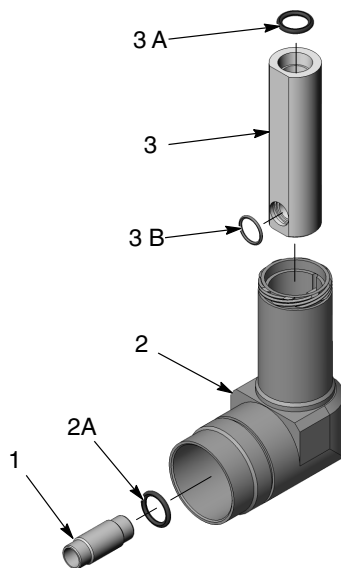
Explosionszeichnung der Baugruppe Verlängerung
